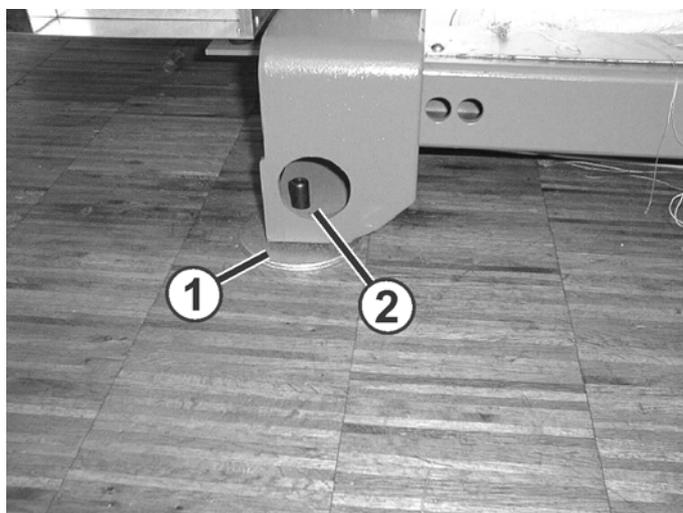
Rondelle en dessous du pied de la machine à tricoter
